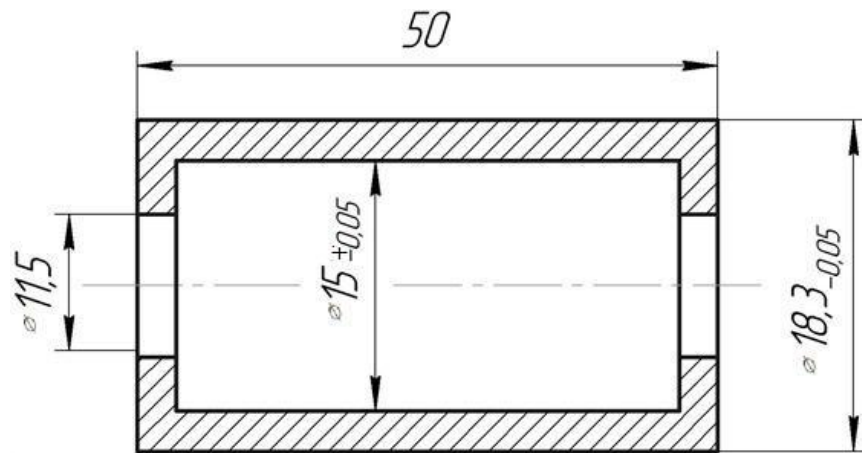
Сталева втулка для пружинного конічного вкладиша
